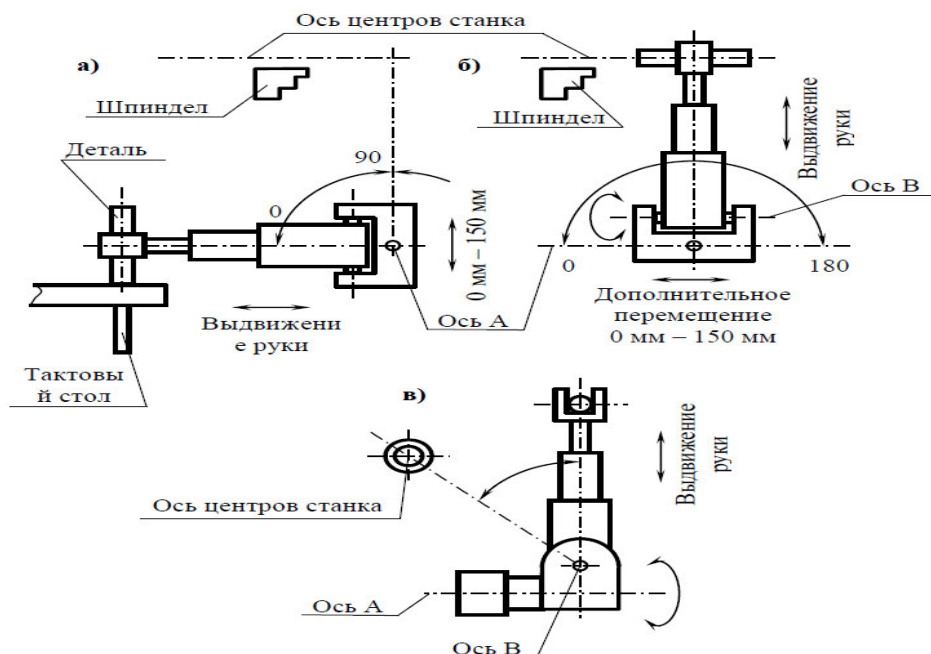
Схема автоматической обрабатывающей ячейки: а – вид спереди (захват заготовки); б – вид спереди (загрузка на станок); в – вид сбоку
